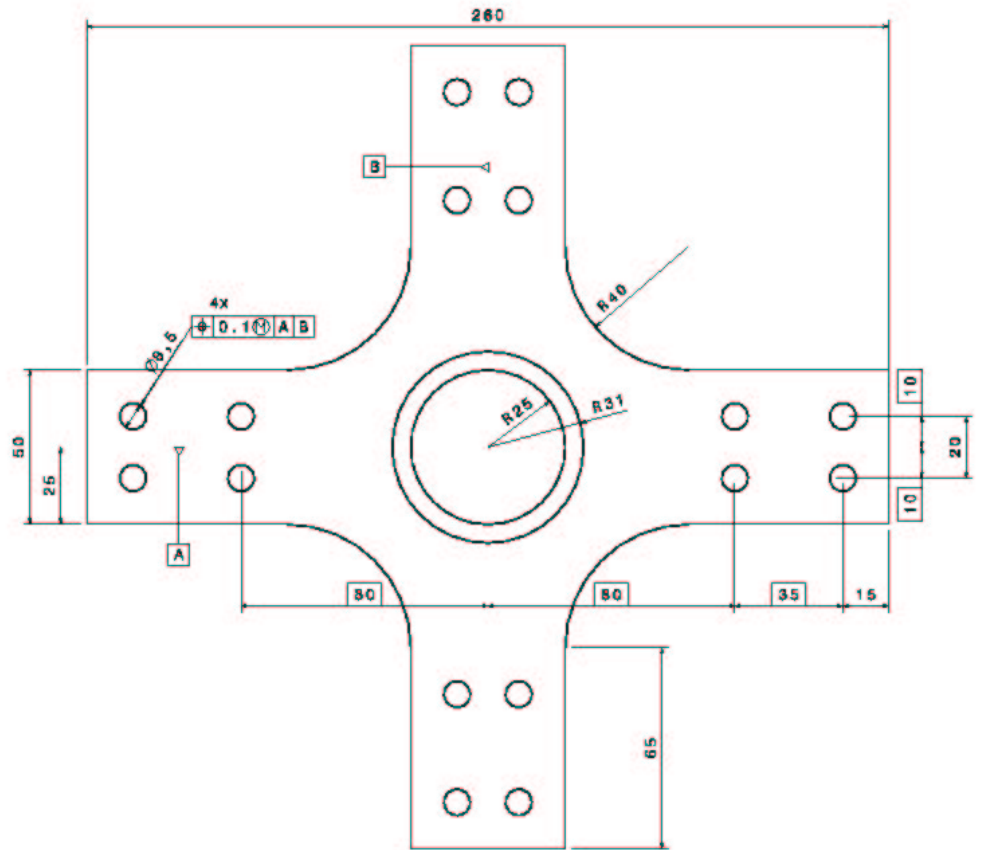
Dessin de définition de l'éprouvette biaxiale réalisée au LMT
